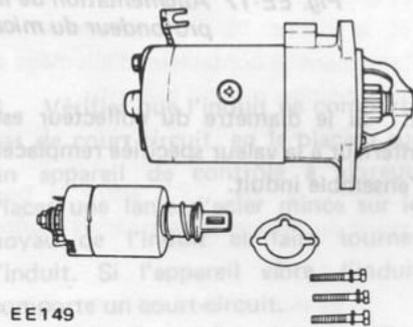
Dépose de l'ensemble interrupteur magnétique
